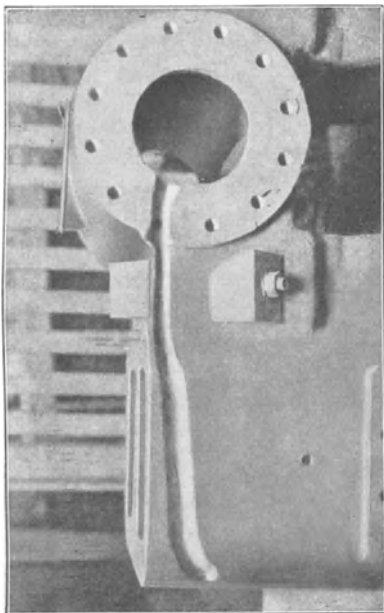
Gußzylinder, zum Schweißen ausgevaut.
